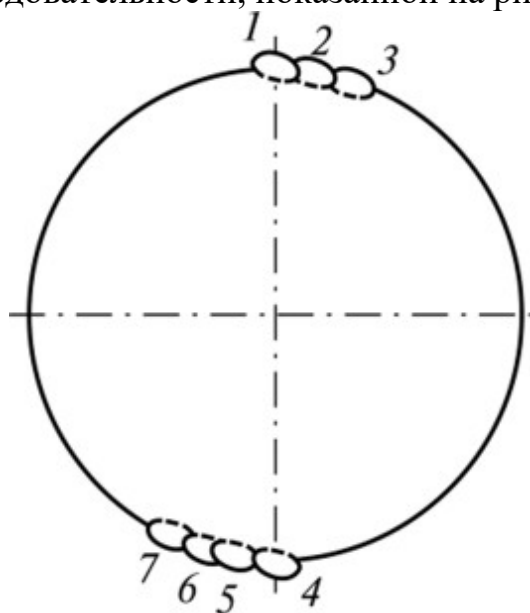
Нанесение наплавочных валиков при восстановлении вала ручной наплавкой
